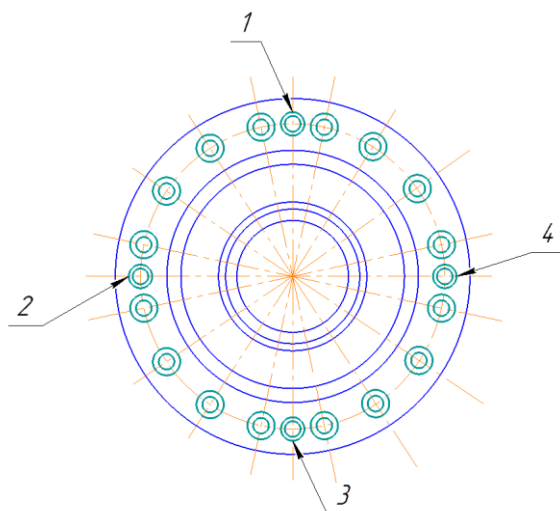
Эскиз координатно-расточной операции с ЧПУ, установ Б
